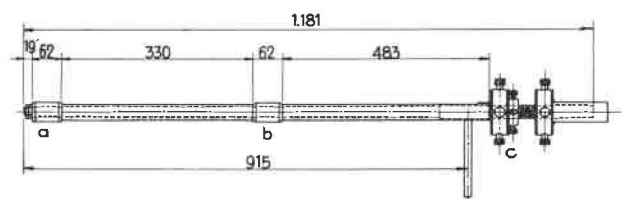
Boulon récupérable Siskol utilisé pour le calage des bossements.
